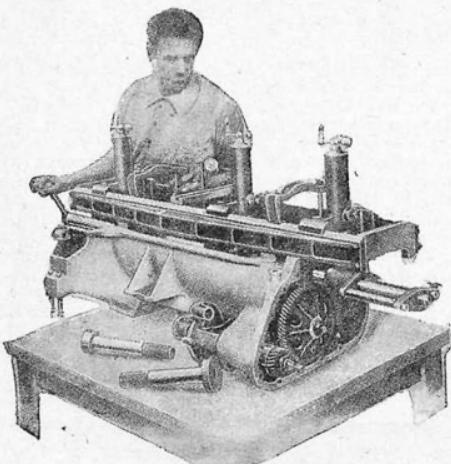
Работа приспособления установленного на картере мотора при расточке коренных подшипников
